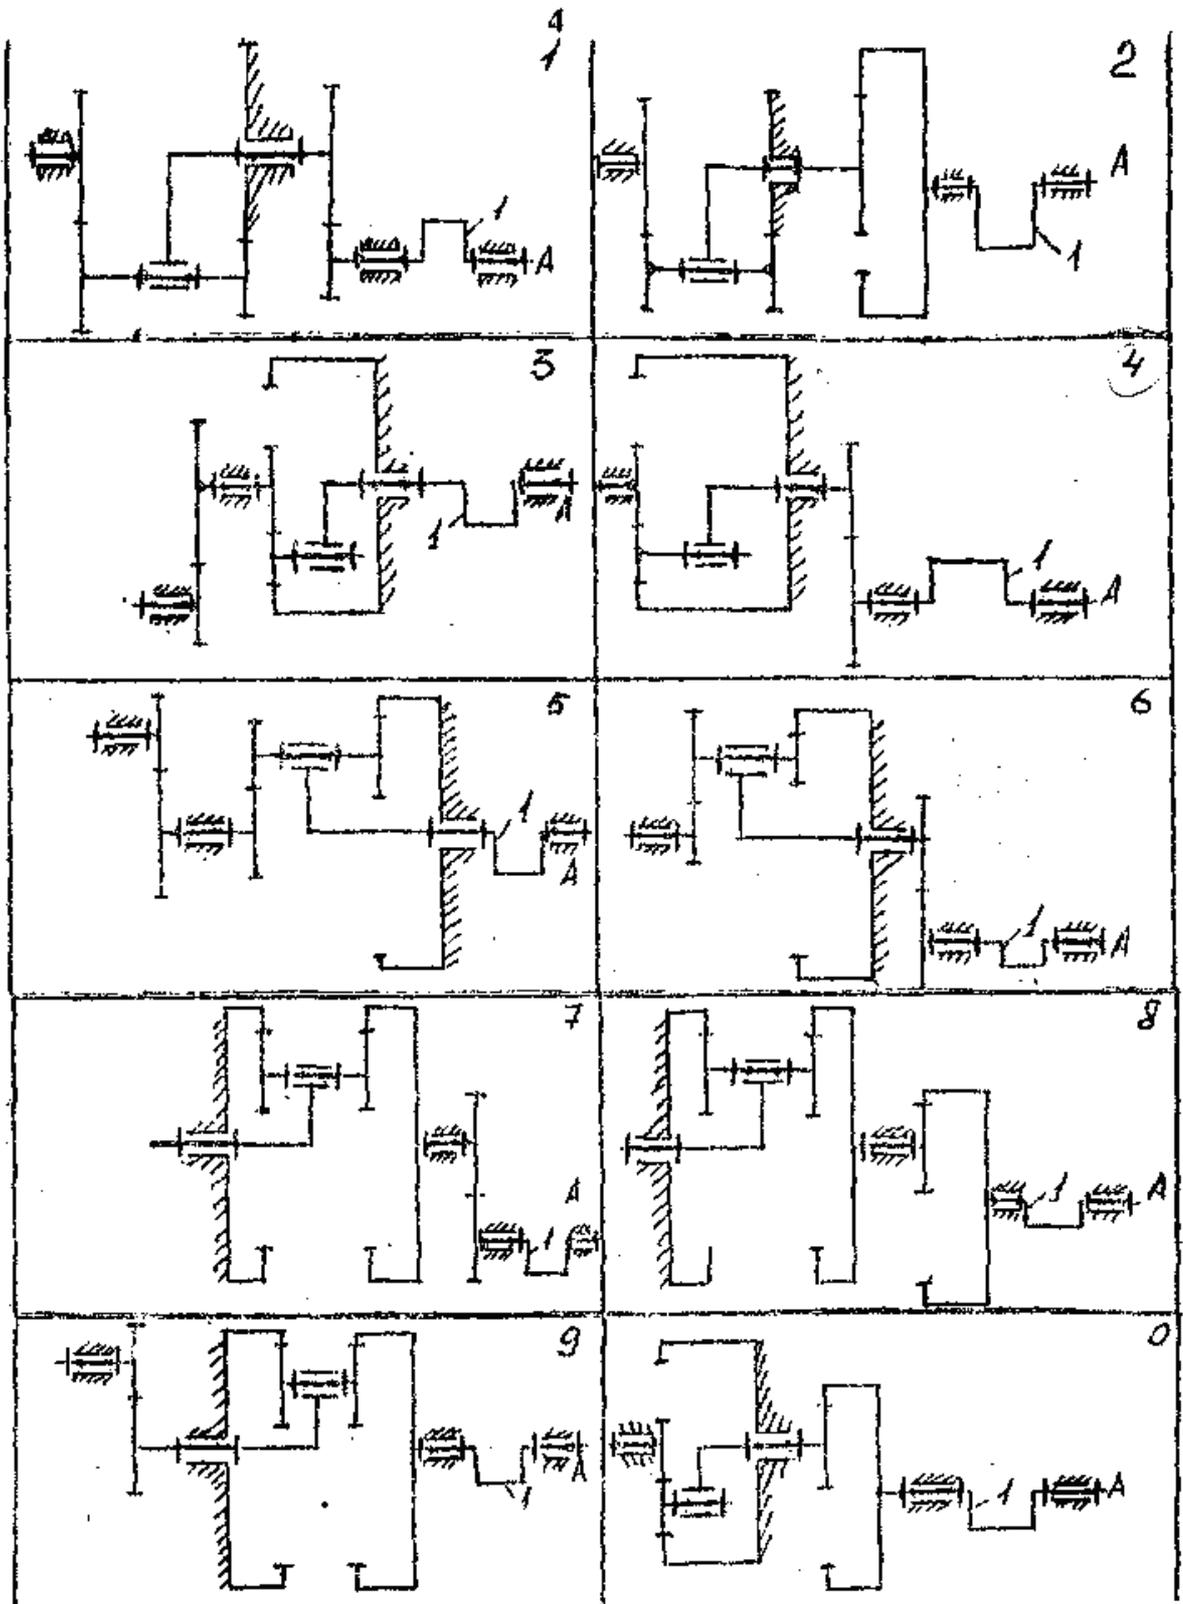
Схемы зубчатых передаточных механизмов (1- кривошип рабочей машины)
